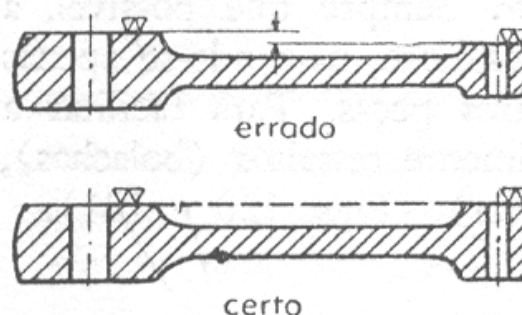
Projeto para que as superfícies de peças fundidas a serem usinadas fiquem no mesmo plano.
